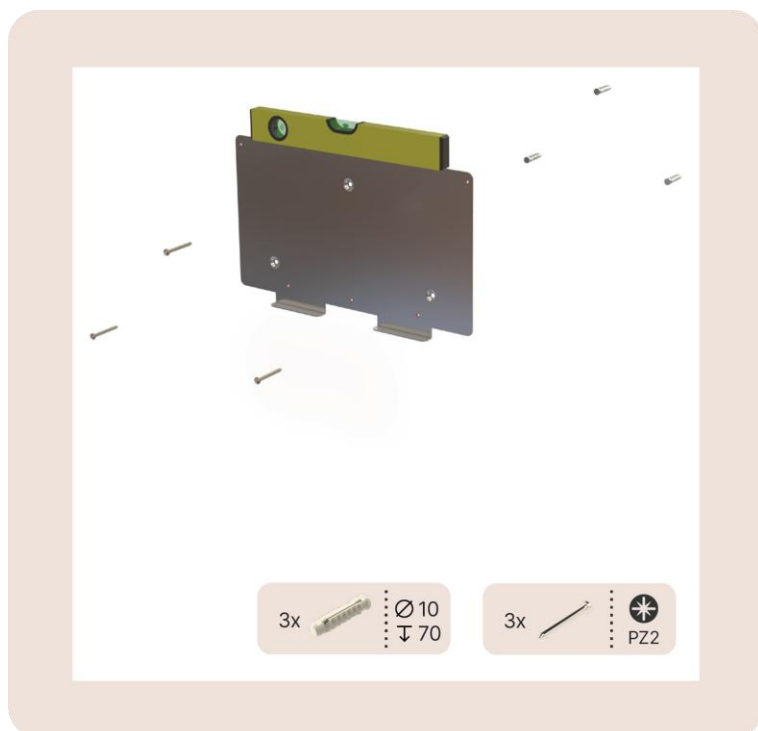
Vue de la platine de fixation murale (A) et d'un niveau à bulle (B)
